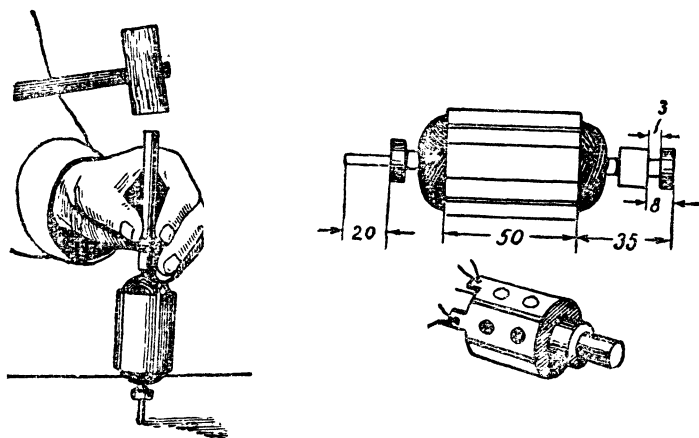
Насадка шариковых подшипников. Собранный ротор двигателя.
